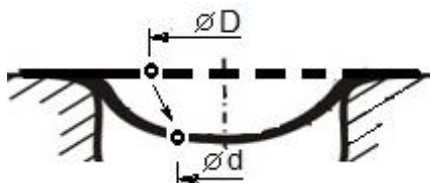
Схема перемещения материальной точки заготовки при штамповке дна
